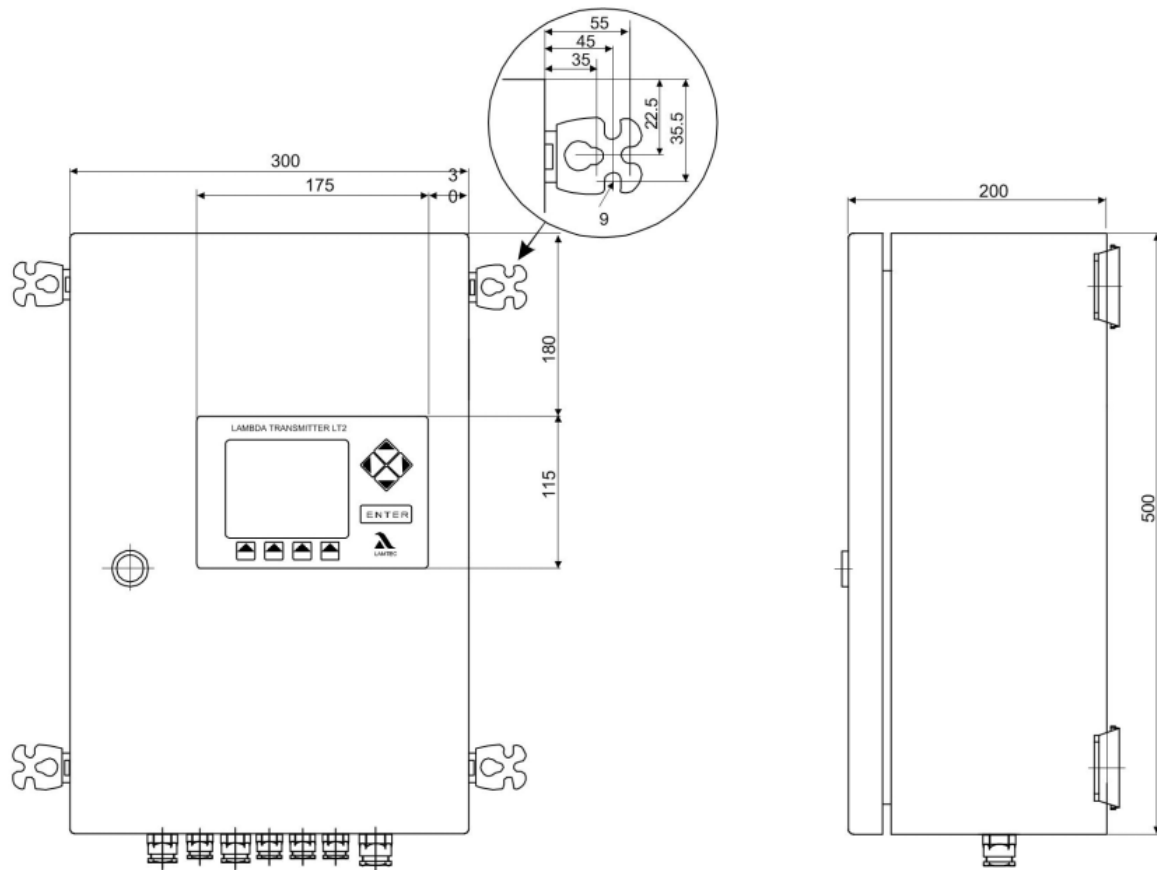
Wandaufbauegehäuse mit Referenzgaspumpe
